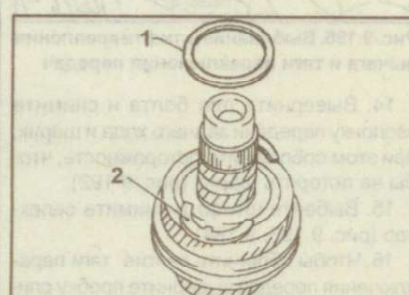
Снятие кольца (1) и упорных шайб шестерни 4-й передачи первичного вала
